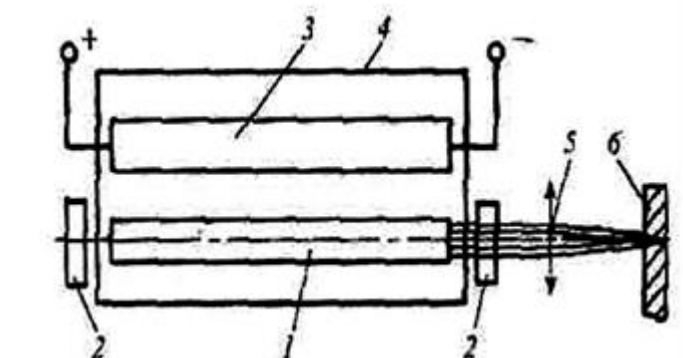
Устройство излучателя твердотельного лазера: 1 - рабочее тело - кристалл; 2 - зеркала резонаторов; 3 - лампа накачки; 4 - отражатель; 5 - фокусирующая линза; 6 - обрабатываемая деталь.
